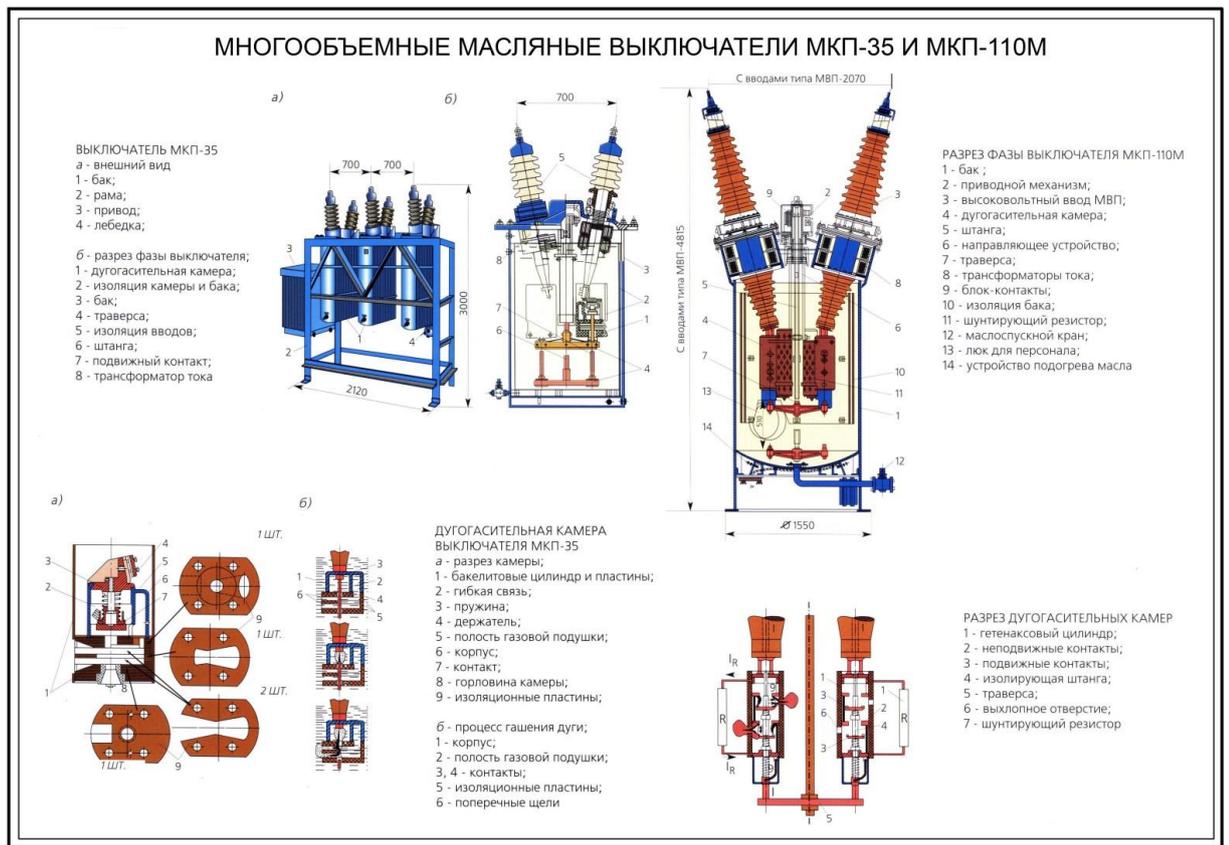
Устройство механизма подвижным частям выключателя
